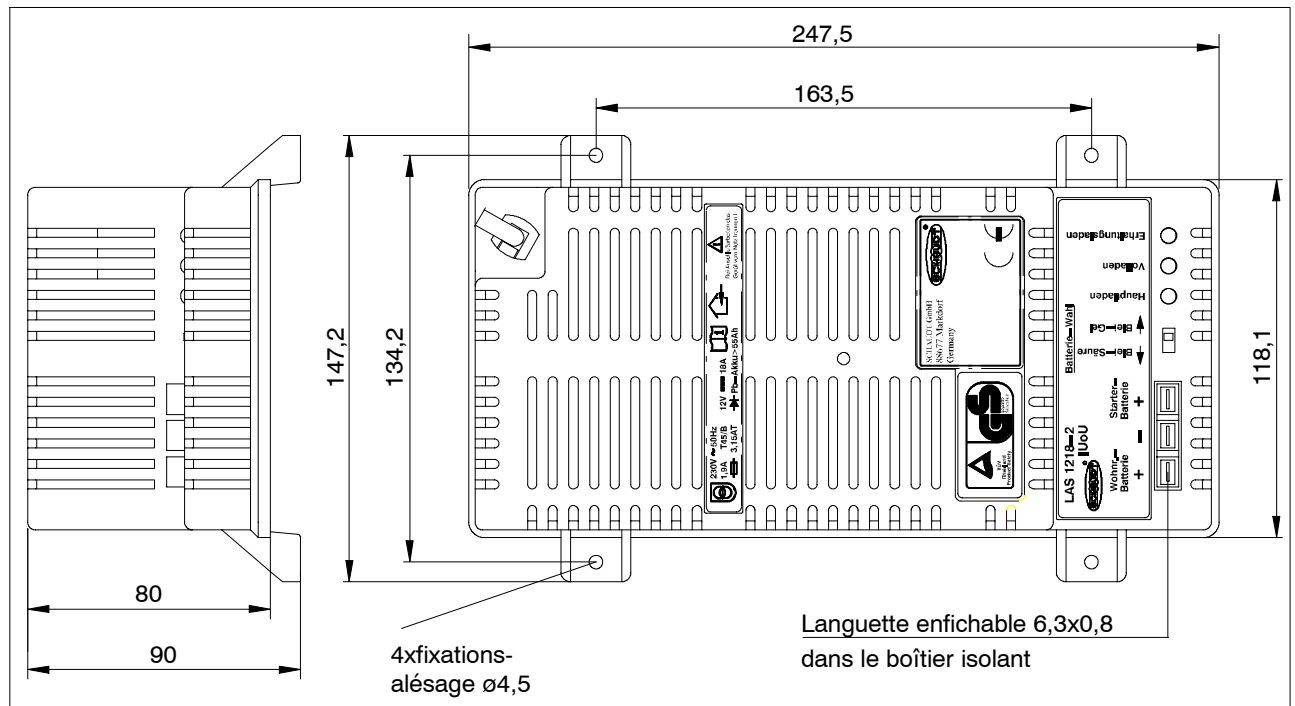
Plan coté du chargeur de batterie LAS 1218-2 (dimensions en mm)
